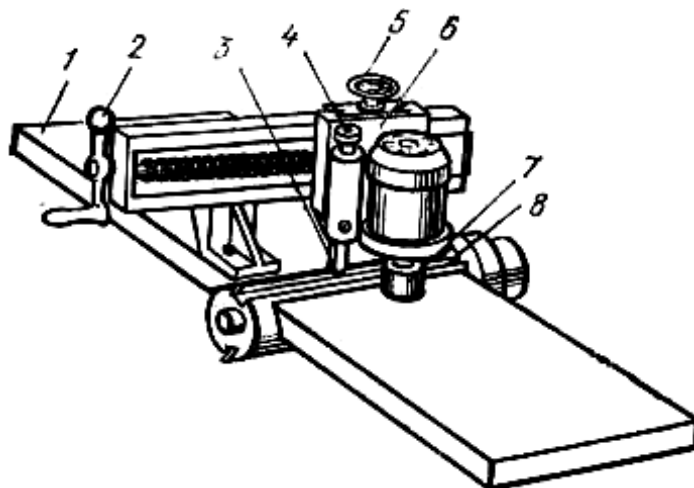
Съемное приспособление для заточки и фугования ножей в ножевом валу фуговального станка: 1 — задний стол, 2 — рукоятка продольной подачи суппорта, 3 — прифуговочный брусок, 4, 5 — маховички поперечной подачи, 6 — суппорт, 7 — заточный круг, 8 — ножевой вал
